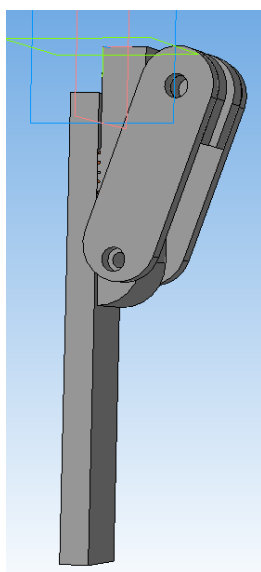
Сварной образец, закрепленный в устройстве
